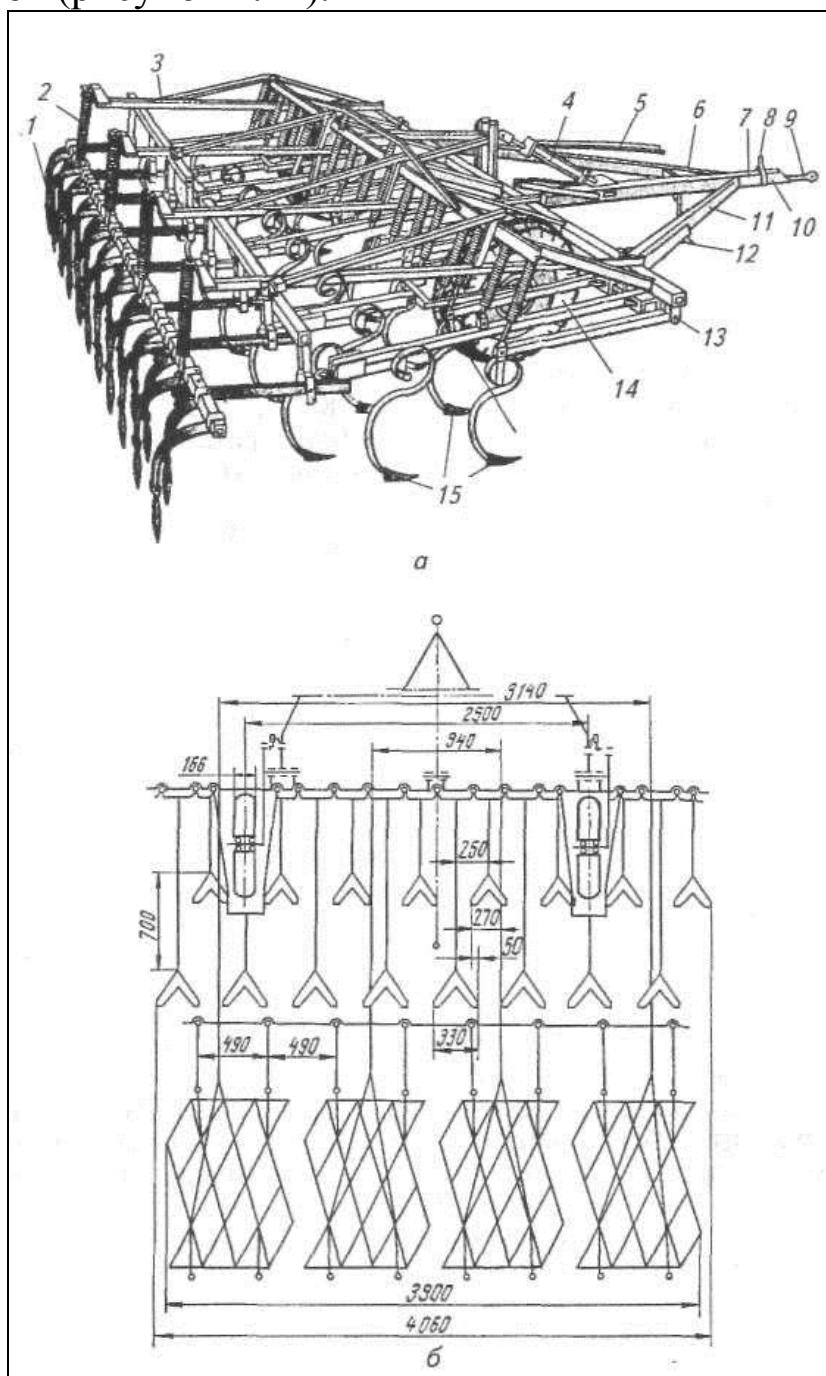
Культиватор КПС-4: а – общий вид; б – схема расстановки рабочих органов (размеры даны в мм); 1 – звено зубовой бороны; 2 – штанга с пружиной; 3 – кронштейн навески; 4 – гидроцилиндр; 5 – штанга гидравлической системы; 6 – левая сница; 7 – центральная тяга; 8 – шлангодержатель; 9 – прицепная серьга; 10 – сница; 11 – правая сница; 12 – подножка; 13 – рама; 14 – опорное колесо; 15 – стрелчатые лапы
